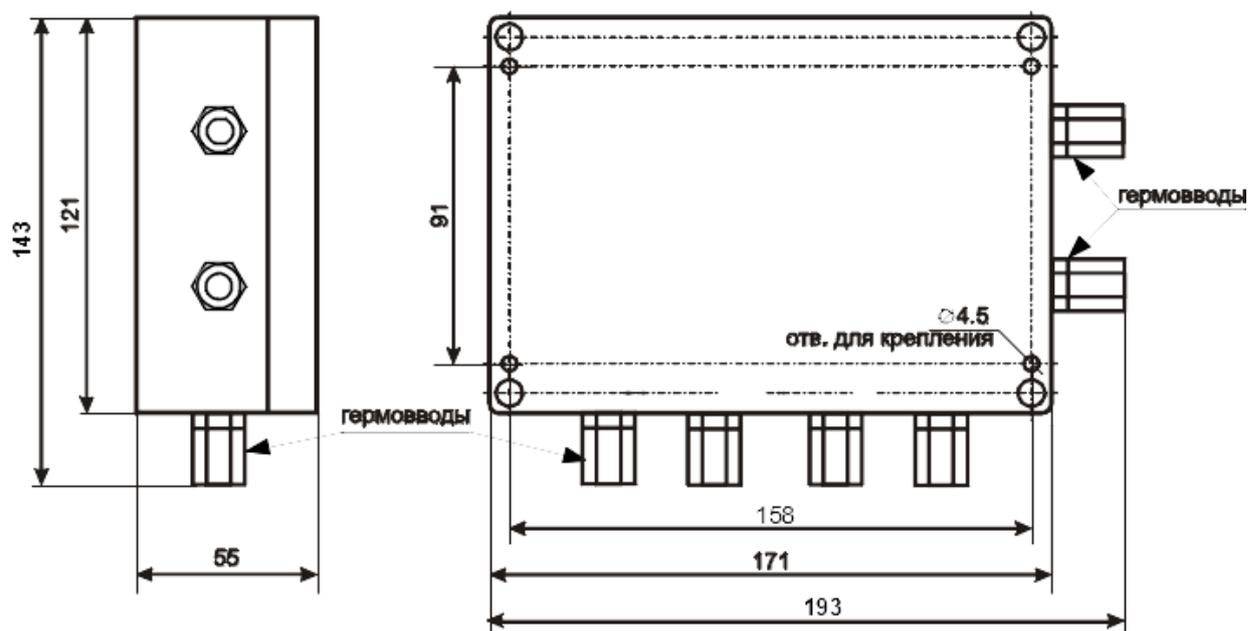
Габаритные и присоединительные размеры КА2, базовый вариант, исп. IP65
